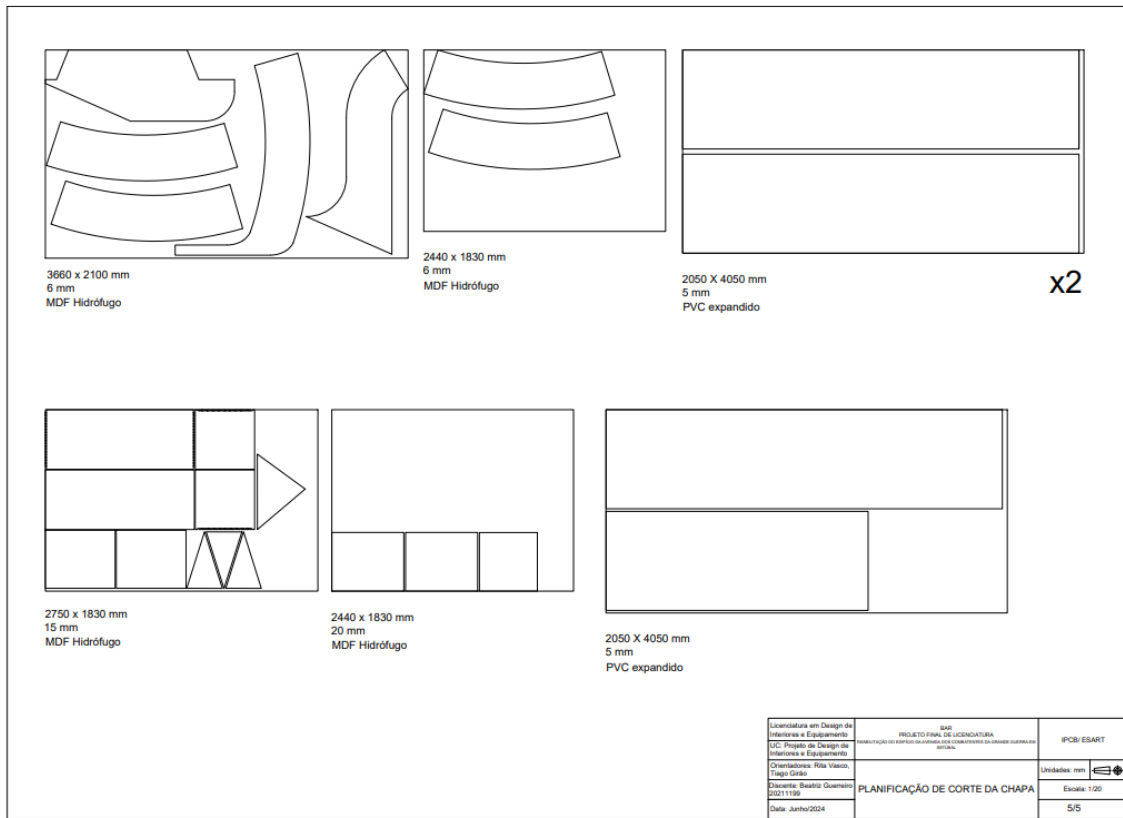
Planificação de corte da chapa, sem escala. Fonte: Autor
